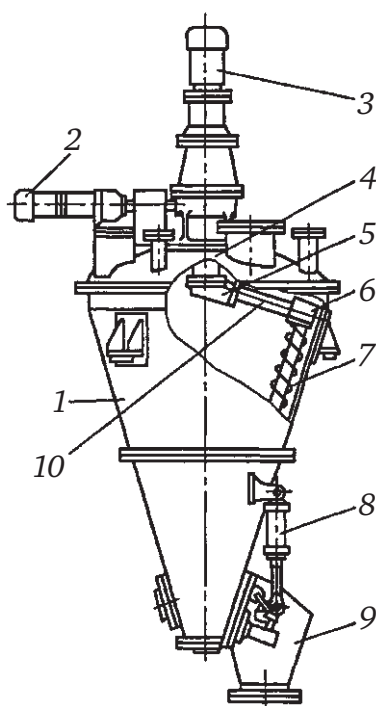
Схема смесителя с планетарно-шнековой мешалкой
